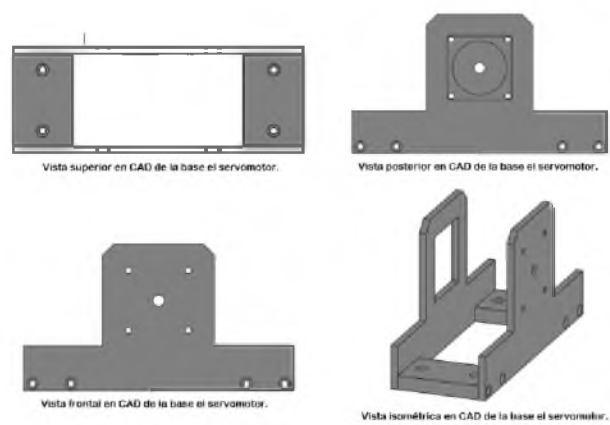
Vistas superior, posterior, frontal e isométrica en CAD de la base el servomotor.
